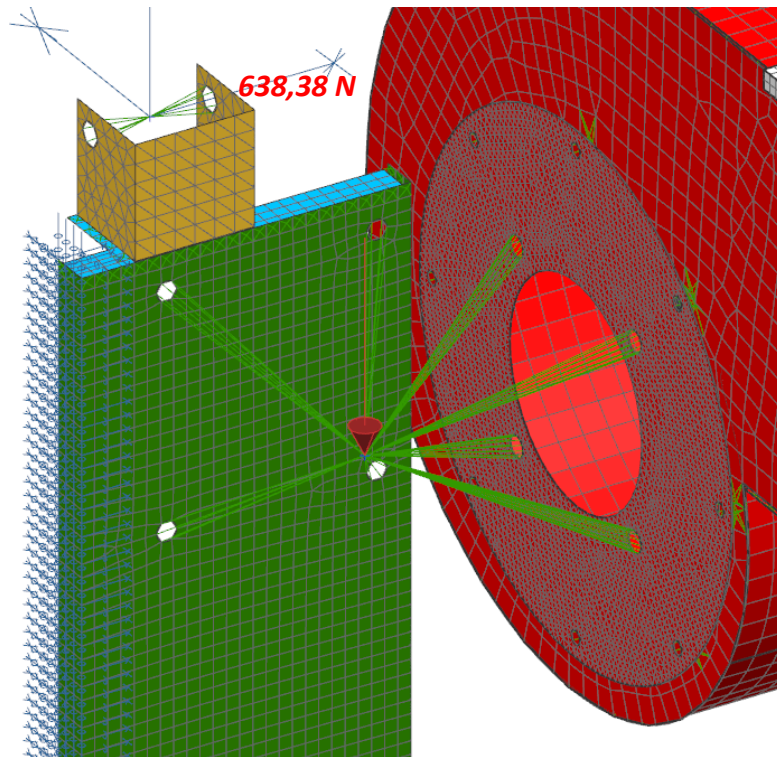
Detalle de fuerza aplicada y punto de aplicación. Conjunto 2. Caso 1.
